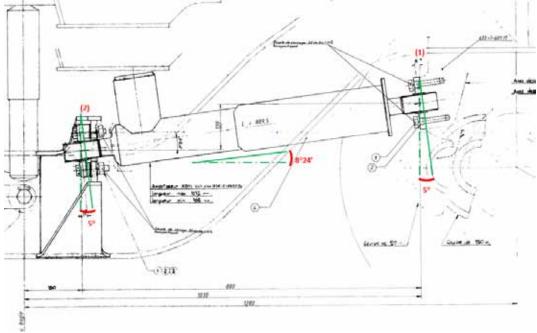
Plan 673-2-125M pour le montage des amortisseurs antilacets
